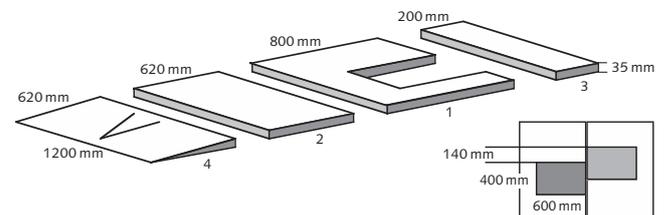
Dimensionen der mobilen Mehrkomponenten Messplattform Typ 9286BA
